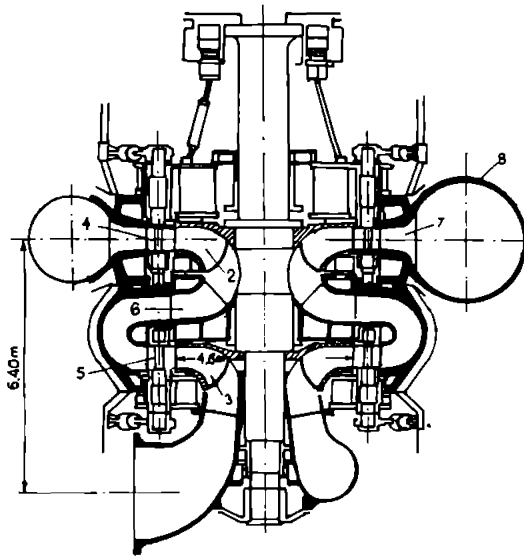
Mașina hidraulică reversibilă cu două etaje din CHEAP Rudlin
